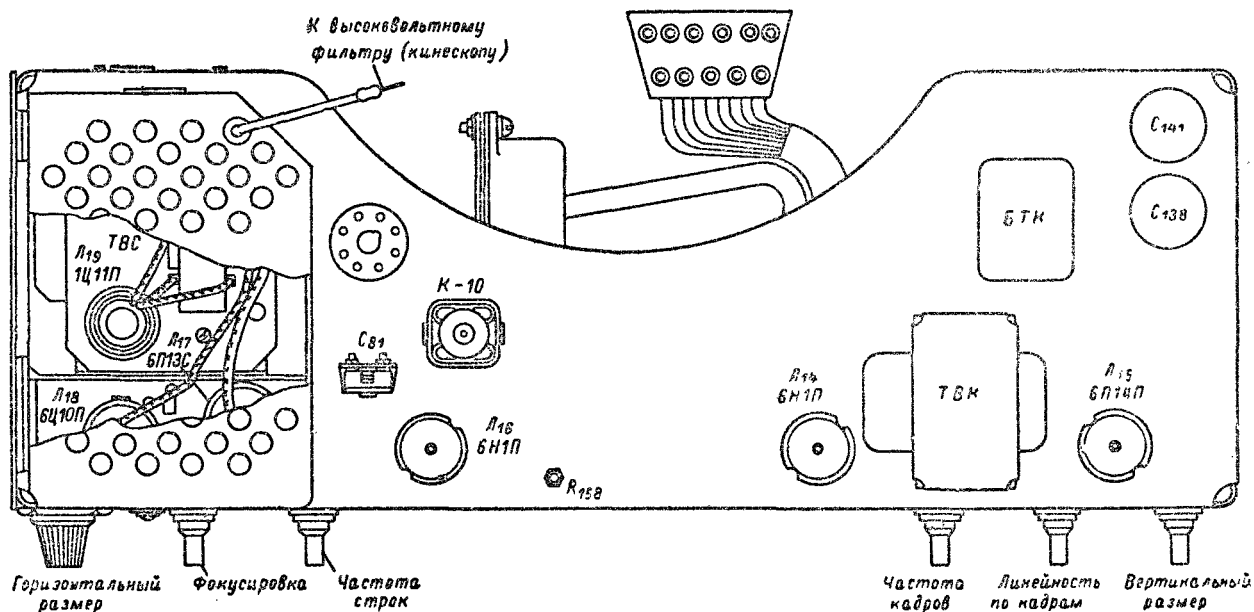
Расположение ламп и деталей на шасси блока развертки телевизора «Рубин-102В» (вид со стороны ламп).
